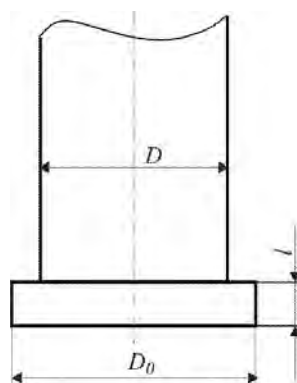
Конструкция инструмента для обработки хрупких материалов на большую глубину
